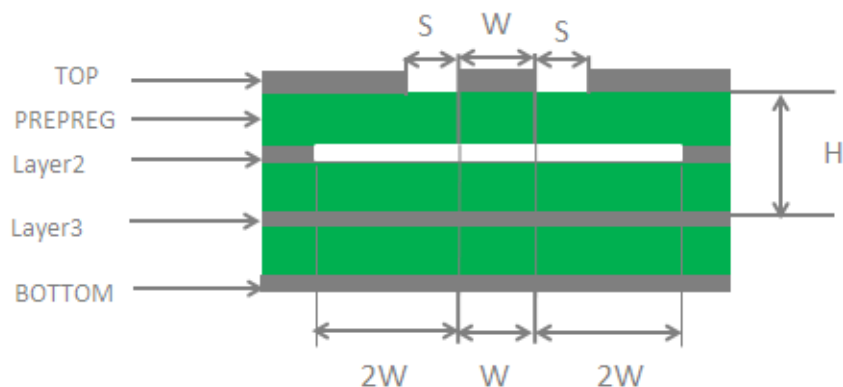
四层 PCB 板共面波导结构 (参考地为第三层)
